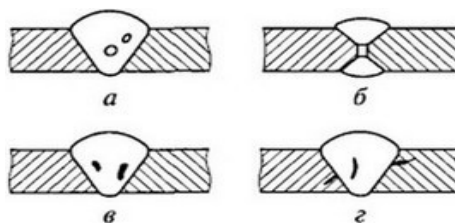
Внутрішні дефекти зварного шва: а пори; б непровари; в шлакові включення; г тріщини
